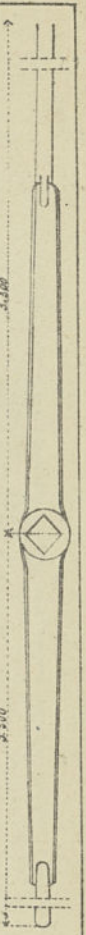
Grue de travail (0.025). Elevation longitudinale.
